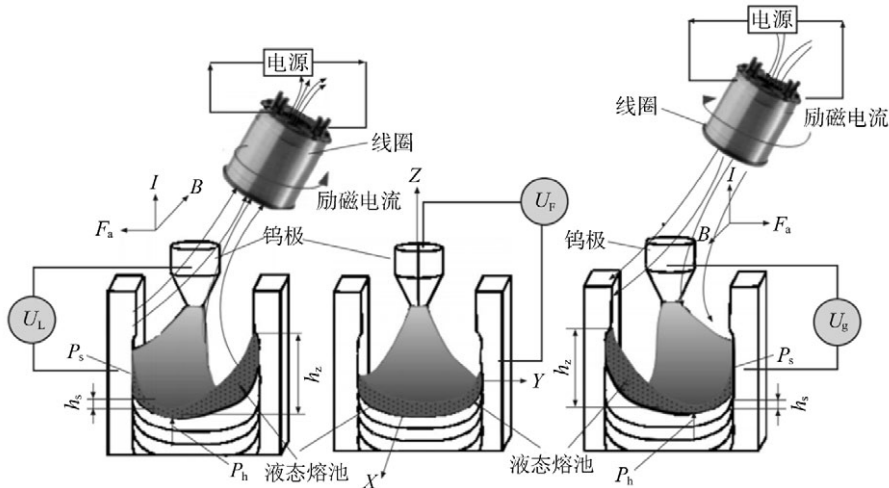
磁控窄间隙 TIG 焊接方法原理
